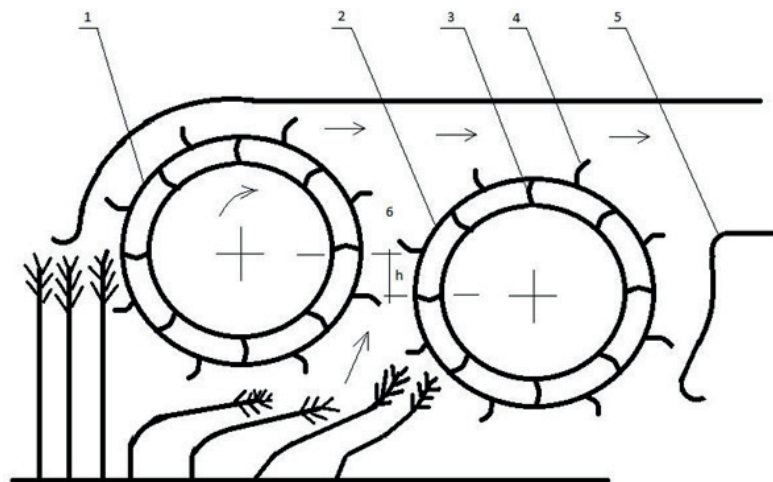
Очесывающее устройство для уборки зерновых культур
